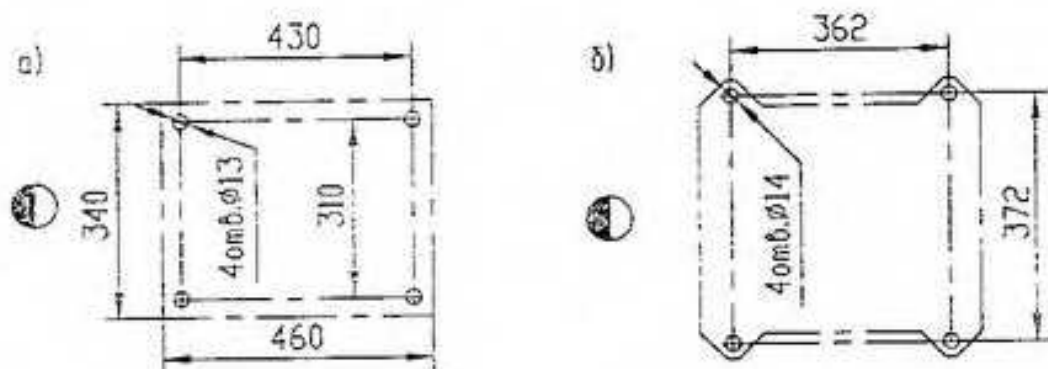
Установочные размеры: а) для станка без тумбы; б) для тумбы.
